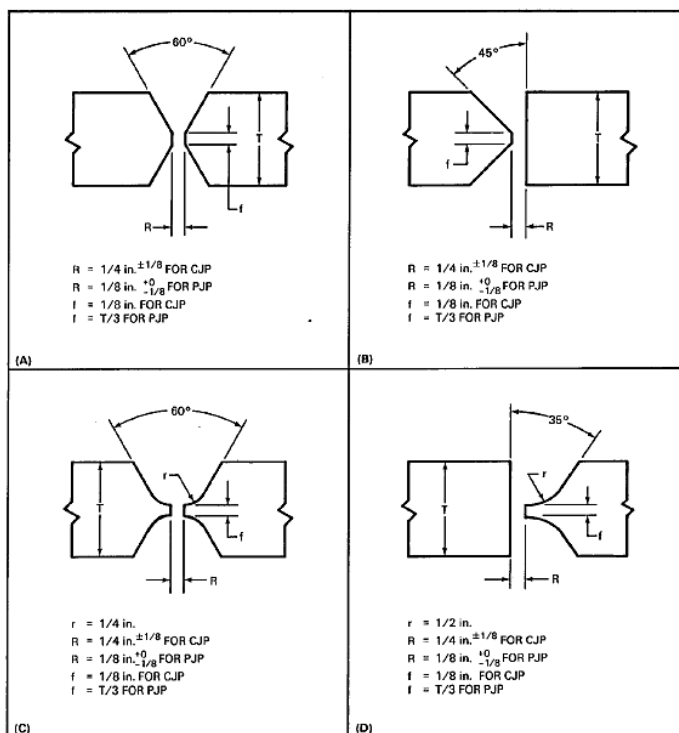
Juntas de soldadura adecuadas para hierro fundido.
